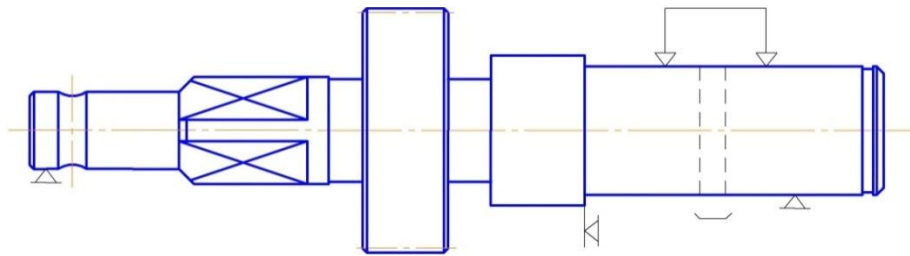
Ескіз обробки деталі на 035 операції.
